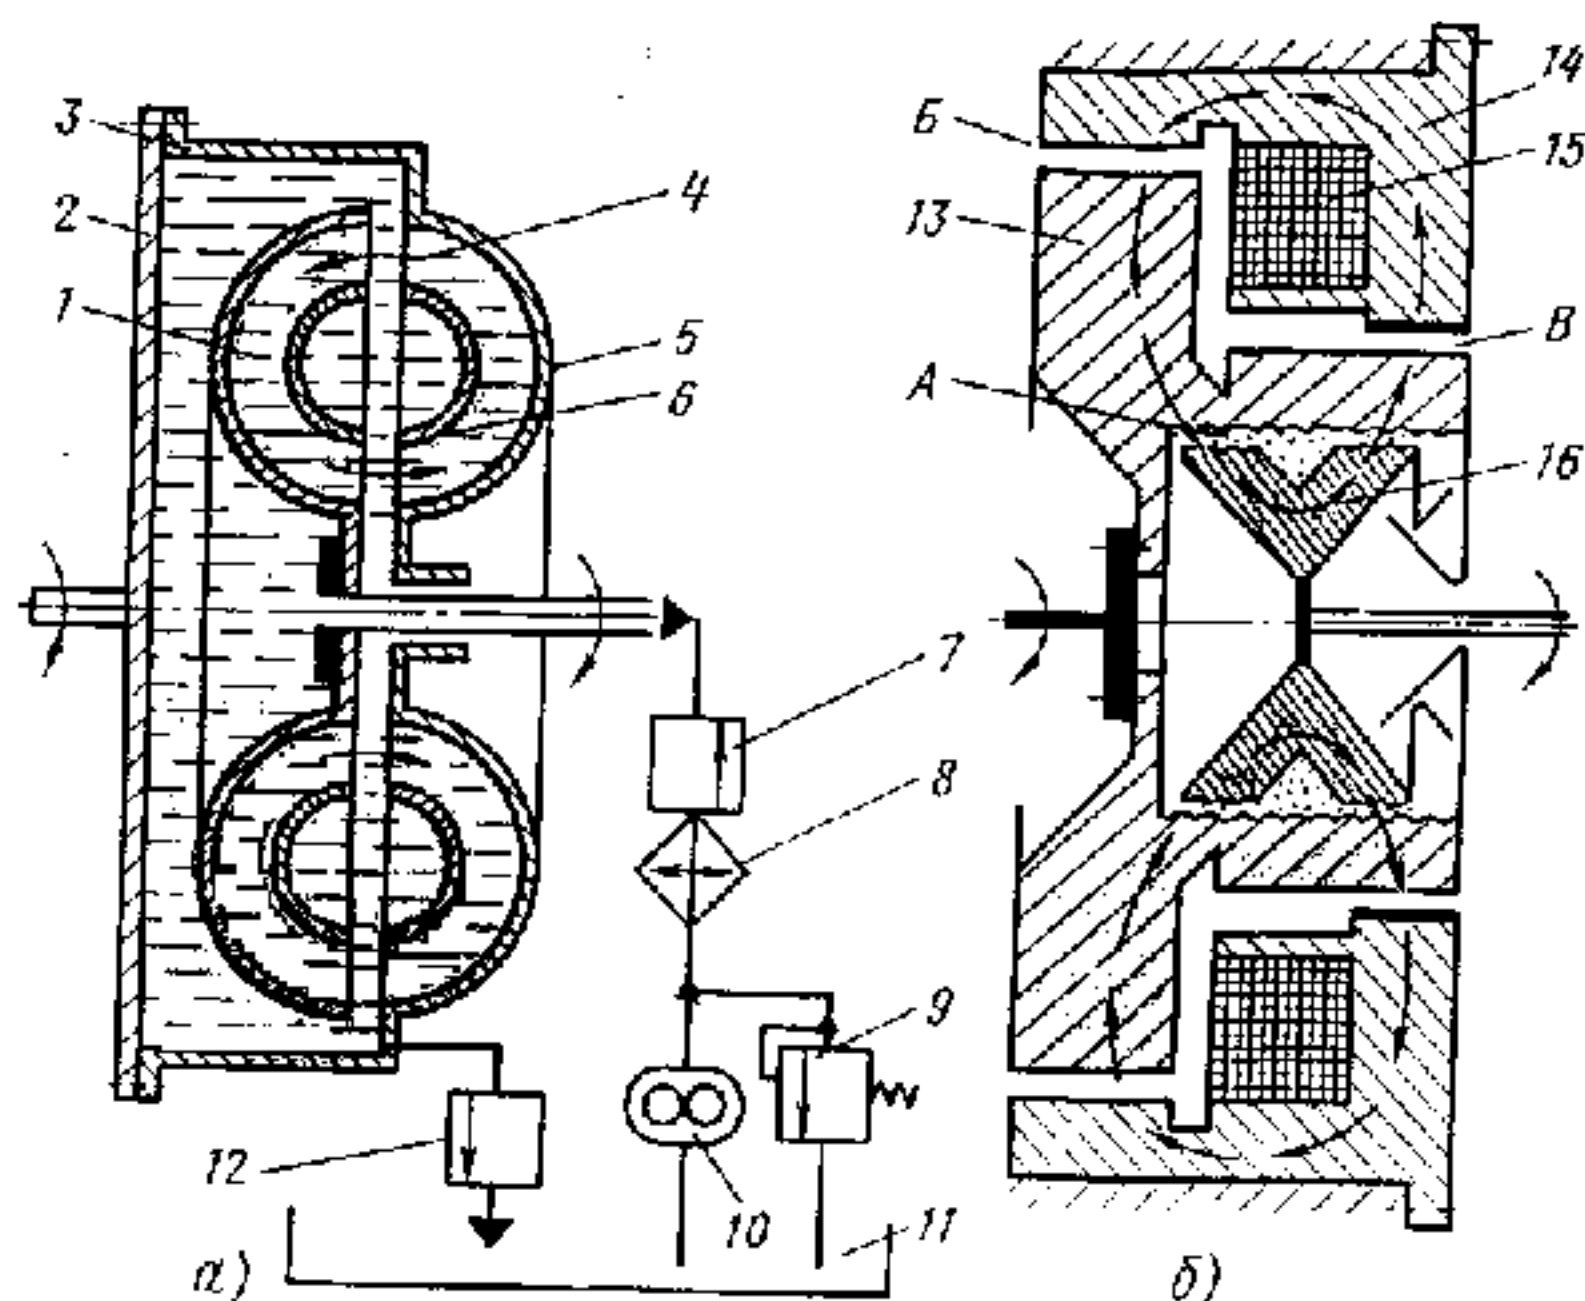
Схемы сцеплений: а — гидравлического; б — электромагнитного порошкового
